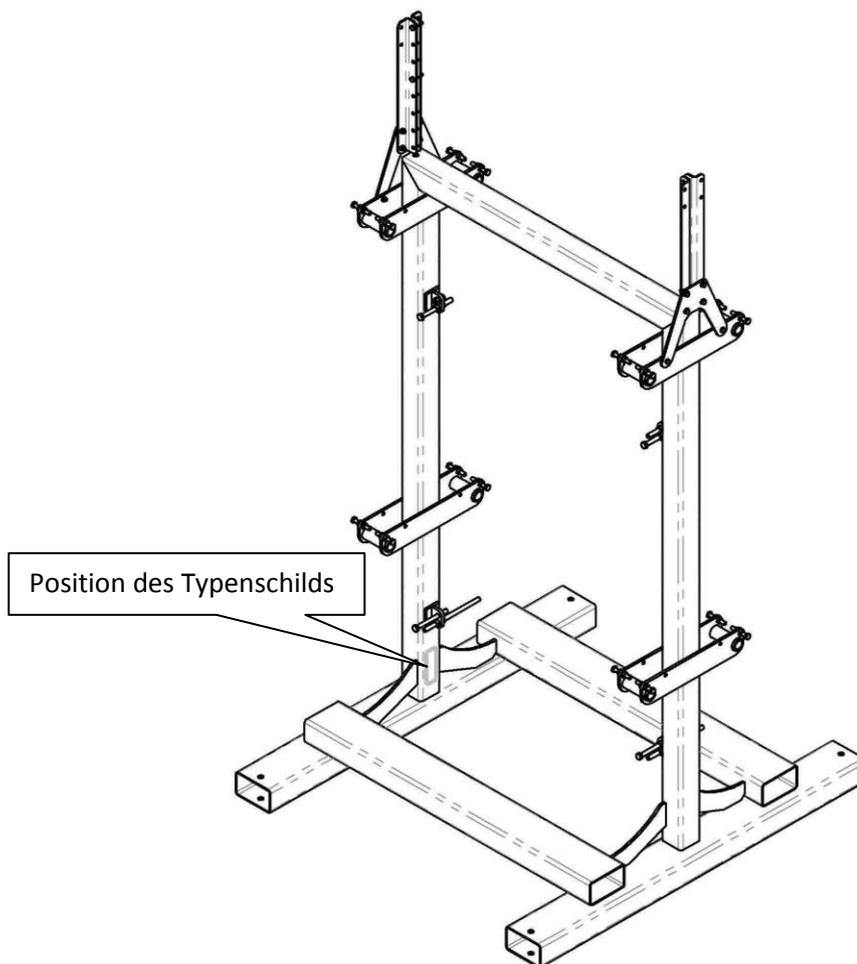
Der aufgestellte Werkzeugständer ohne Frontlader Werkzeuge
